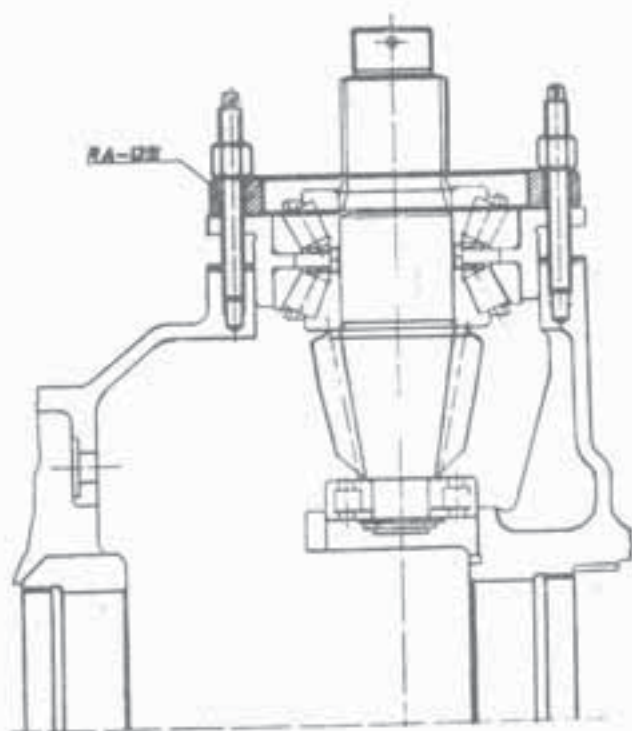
Напрессовка внутреннего кольца конического роликоподшипника
